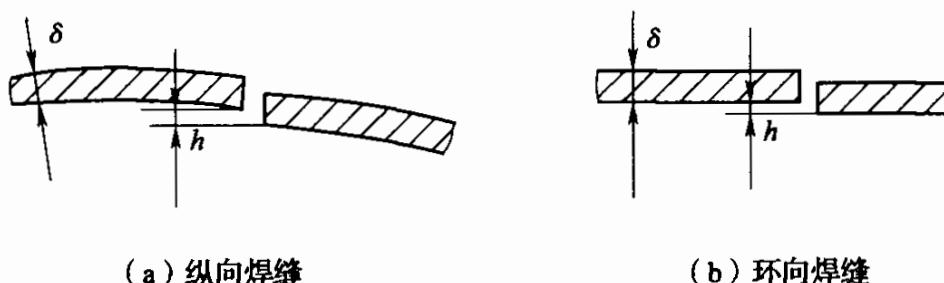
钢板的焊缝对口错边量
